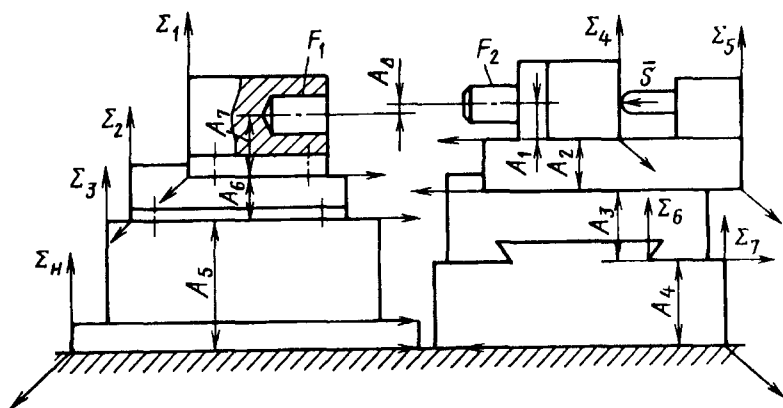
Координатные системы сборочной машины для соединения вала с втулкой
